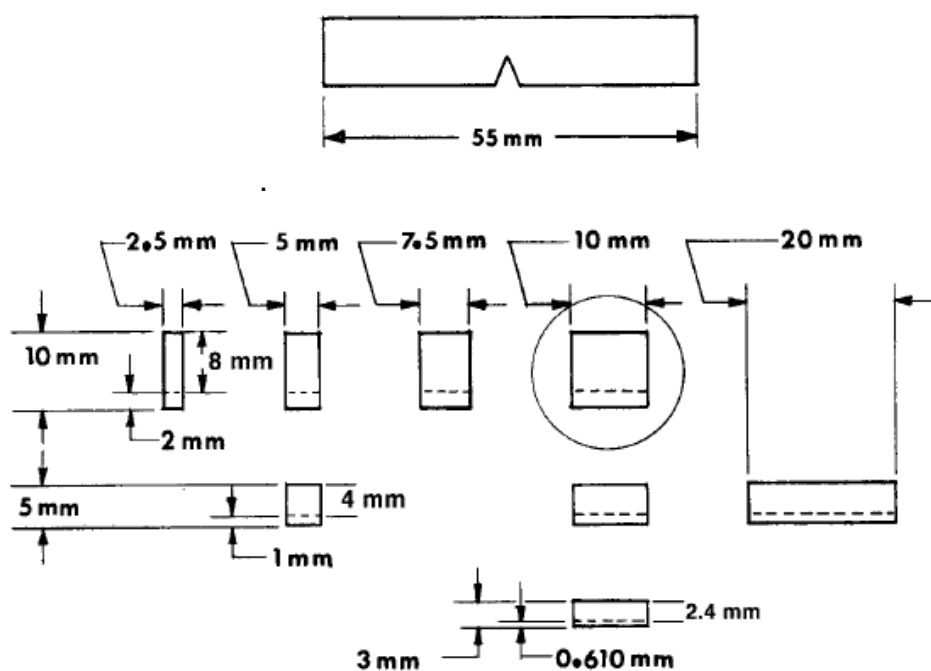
DESENHO ESQUEMÁTICO DO PROVA DE IMPACTO CHARPY (ASTM E23)
